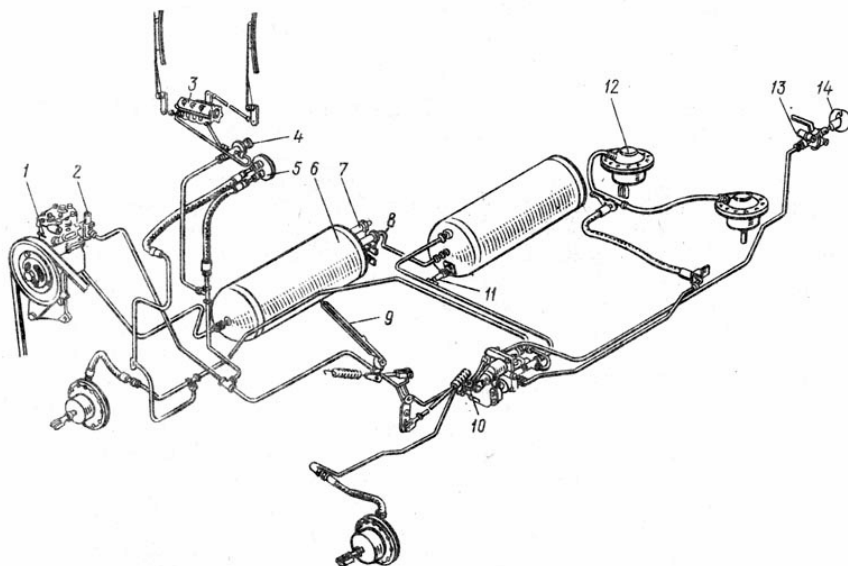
Пневматический привод тормозов автомобиля ЗИЛ-130
